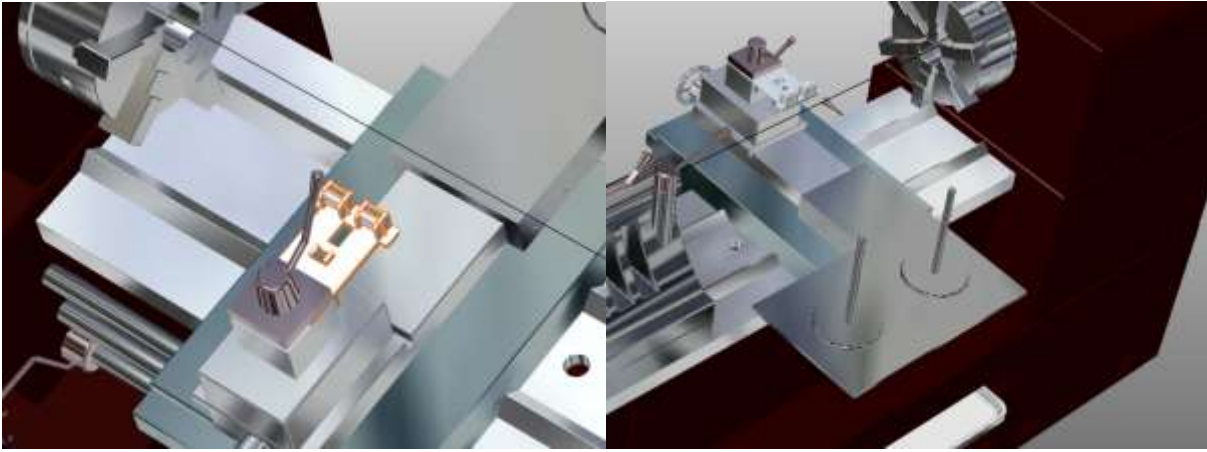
Пристосування для виготовлення елементів каркаса встановлений на верстат
